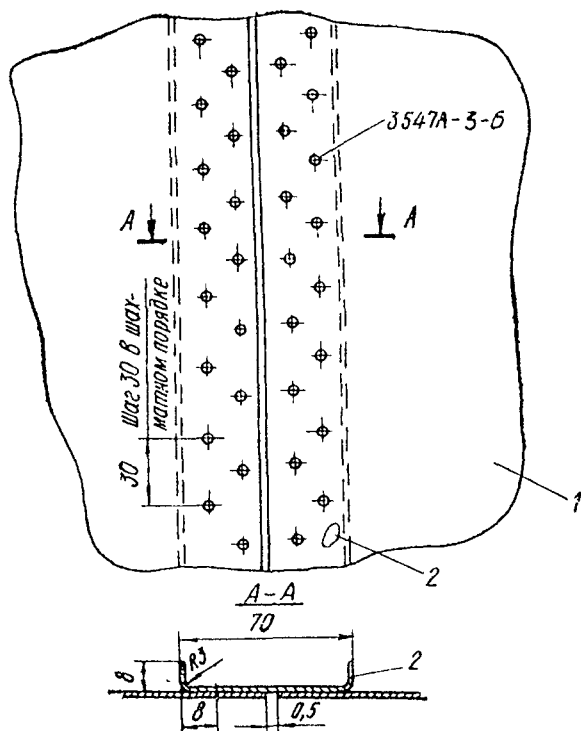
Стык обшивки: рулей, элеронов, закрылков посредством стыковой ленты:
